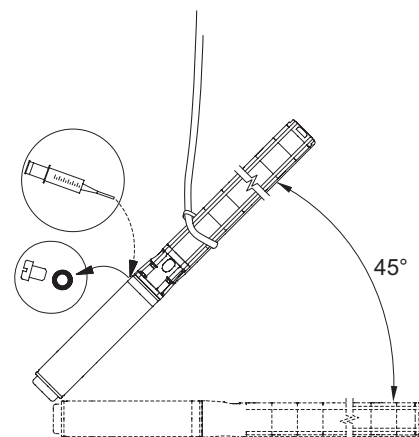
Posición de la bomba durante el llenado – MS 6000
